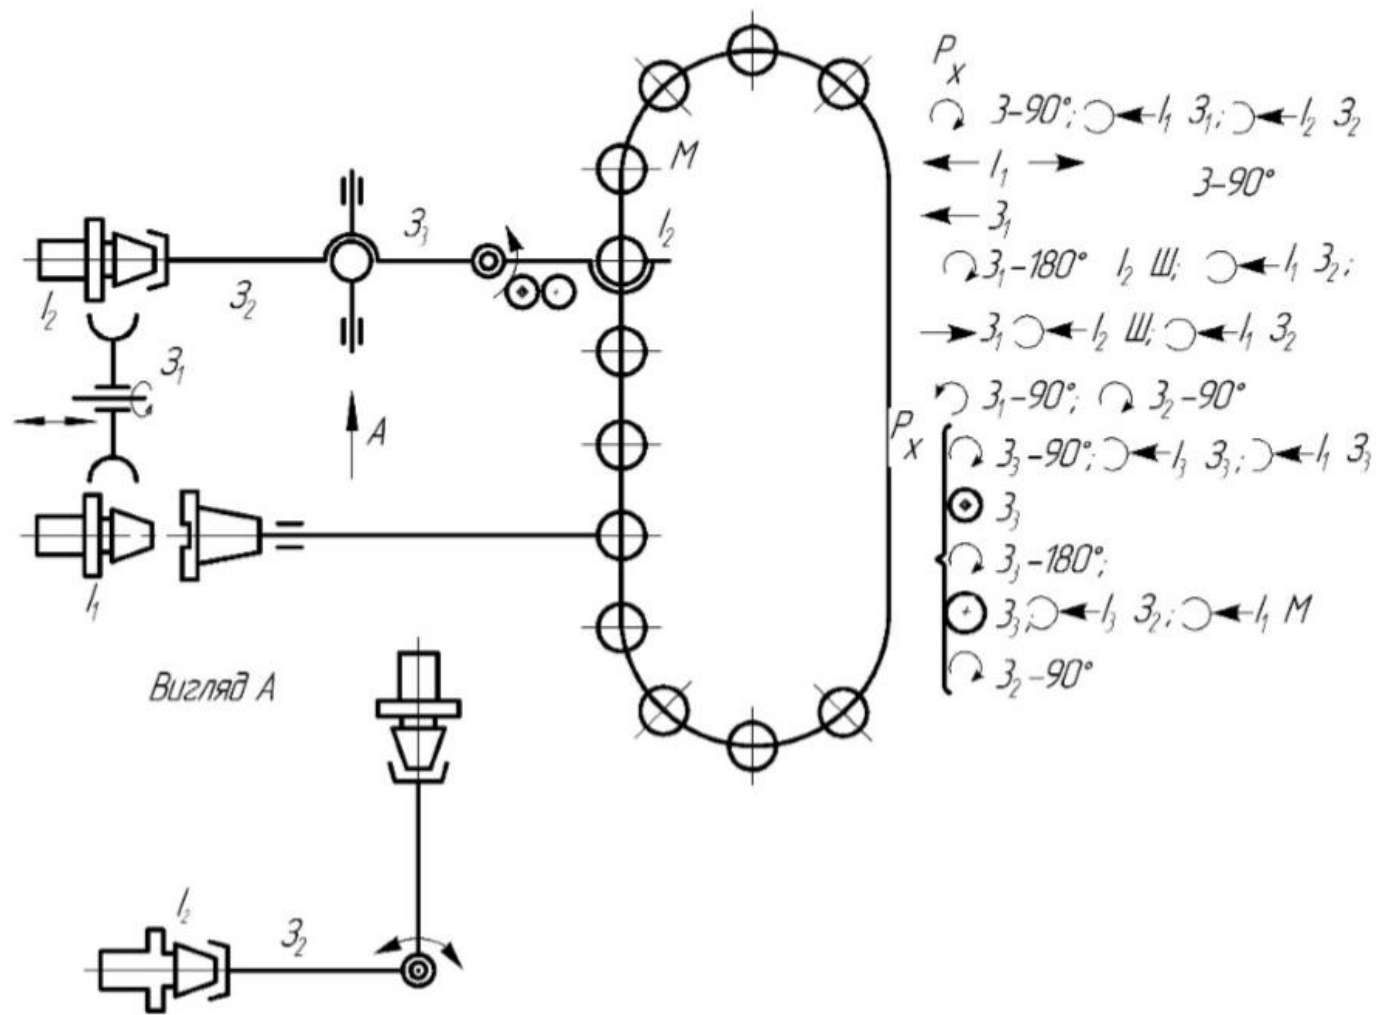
Механізми з захватними пристроями біля шпинделя
